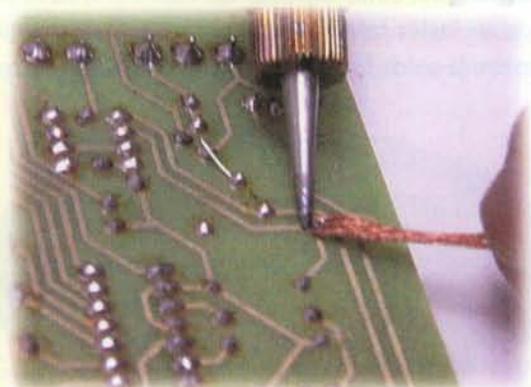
Retirando la soldadura con la cinta de cobre trenzada
